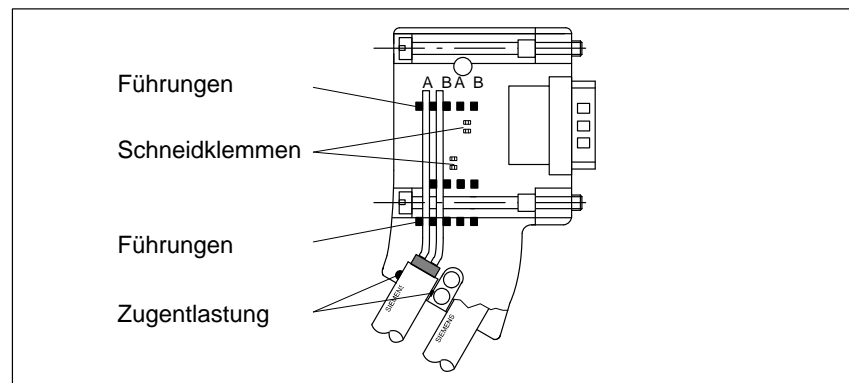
Buskabel am Busanschlußstecker (6ES7 972-0BA30 ...) anschließen
